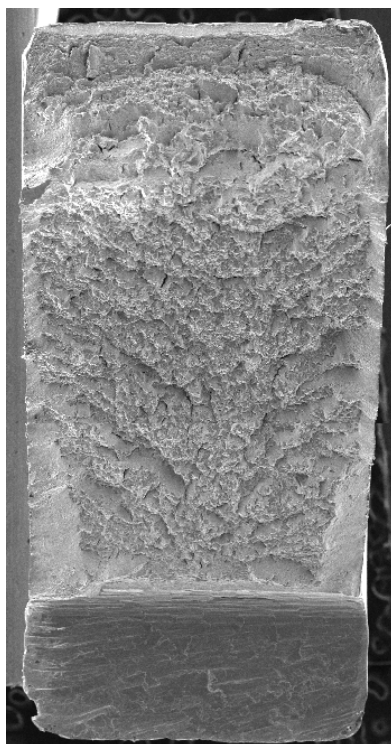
Superficie de fractura de la probeta B7-A-3.
